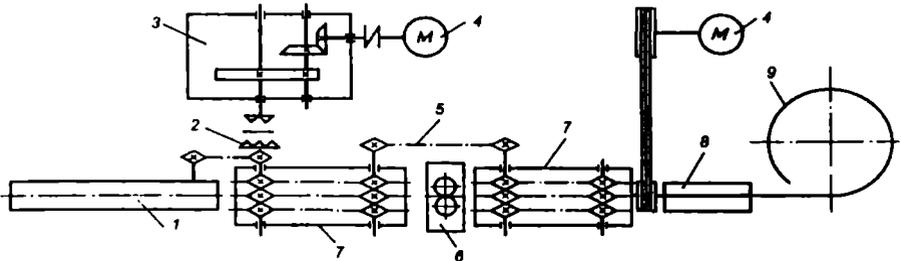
Кинематическая схема правильно-отрезного станка конструкции ЦНИИОМТП:
